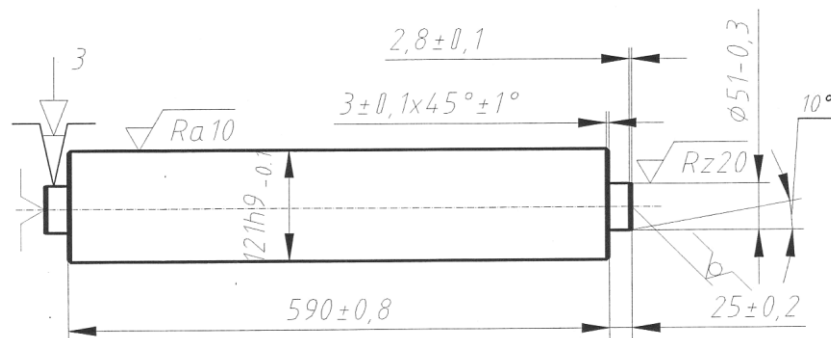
Ескіз обробки деталі операція №030
